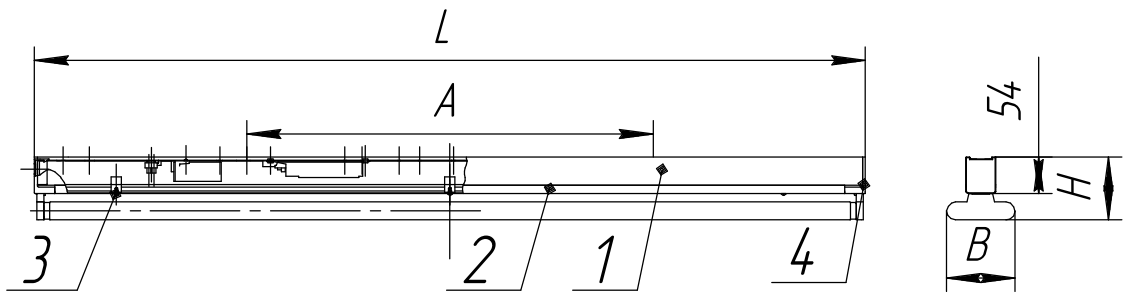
1. Корпус в сборе, 2. Крышка, 3. Винт, 4. Крышка.
